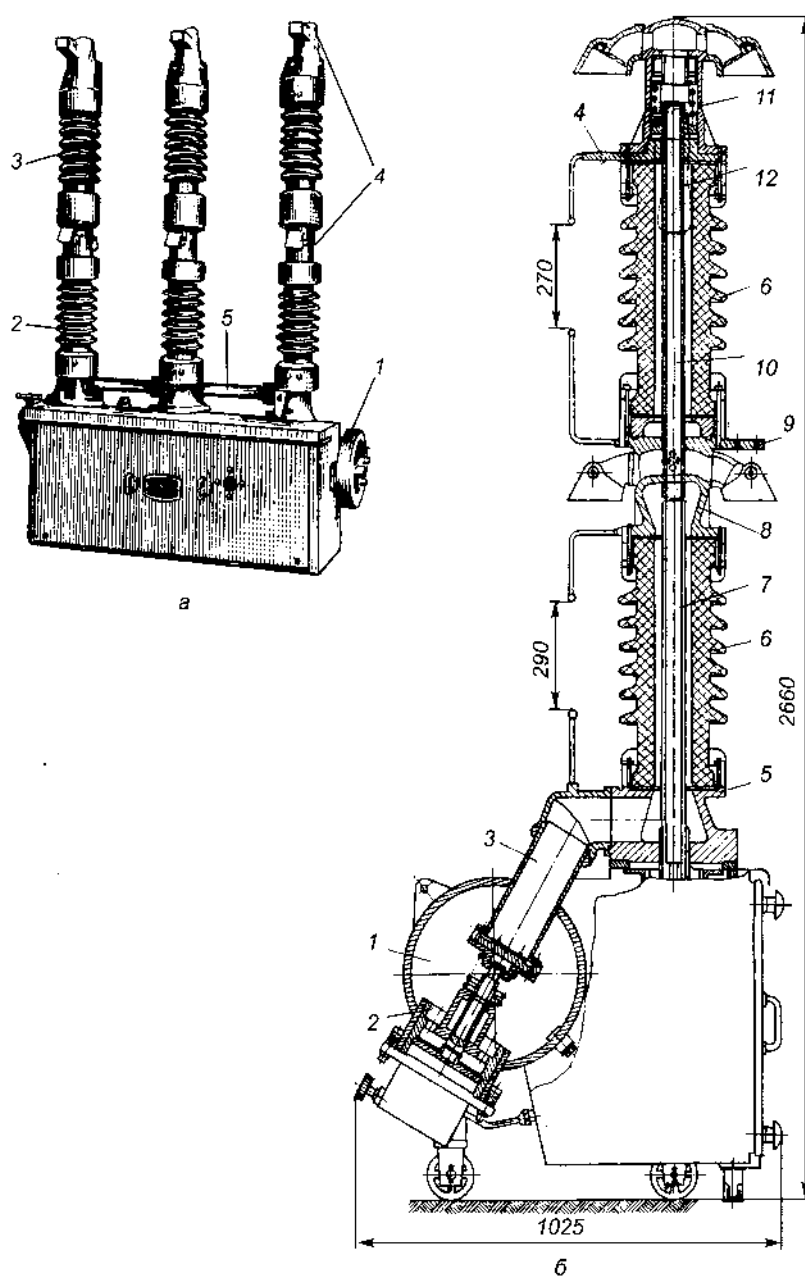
Воздушный выключатель ВВН-35: а) – общий вид: 1 – тележка с резервуаром для сжатого воздуха; 2 – опорный изолятор; 3 – гасительная камера; 4 – выхлопные патрубки; 5 – трубопровод сжатого газа; б) – резервуар по среднему полюсу; 1 – резервуар сжатого воздуха; 2 – клапан; 3 – воздухопровод; 4 – верхний наконечник; 5 – нижний фланец; 6 – верхний фланец; 7 – изоляционная штанга; 8 – верхний фланец; 9 – нижний наконечник; 10 – контакт отделителя; 11 – головка; 12 – гасительный контакт
